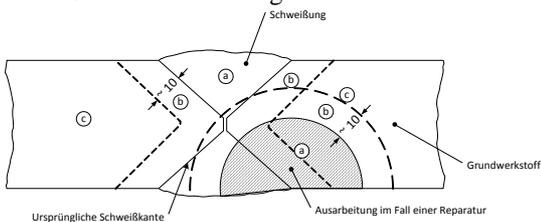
Fertigungsschweißung und Schweißnahtreparatur
